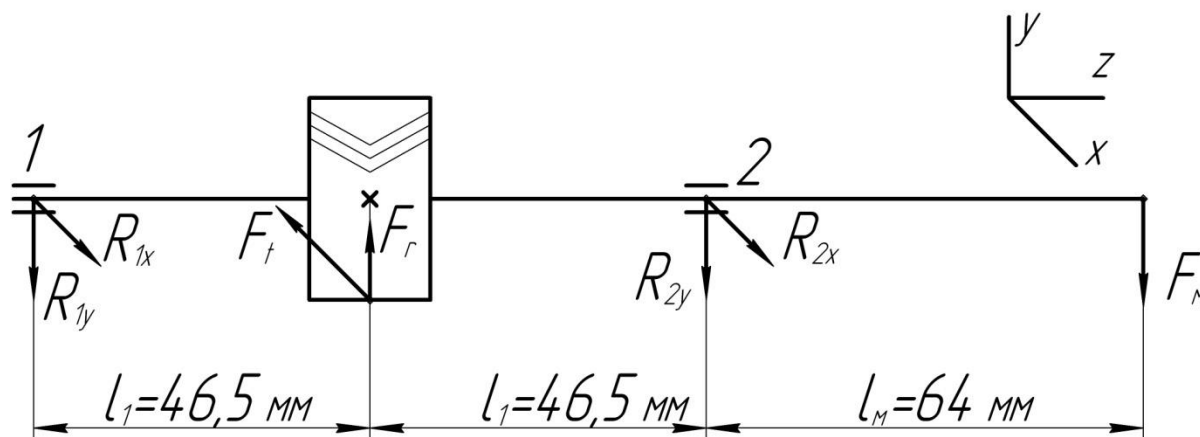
Расчётная схема ведущего вала редуктора.
